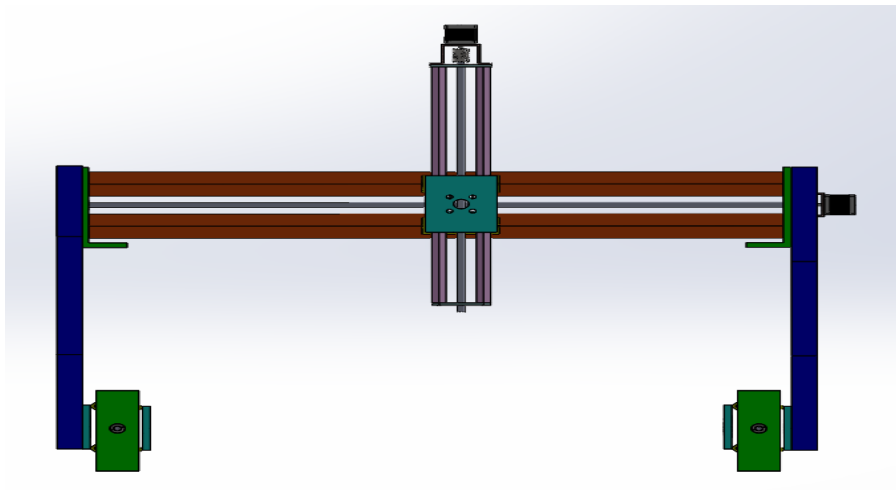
مسقط منظوري مجمع للمحور Z.
